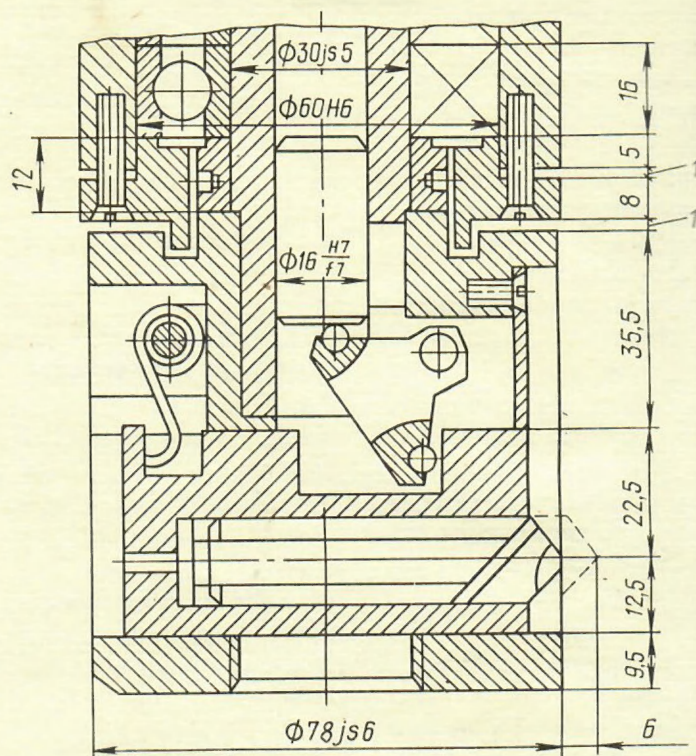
Присоединительные размеры резцовой головки шпинделя
